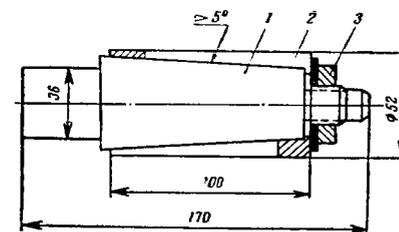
Притир для диаметра цилиндра 52 мм: 1—корпус притира; 2—размерная конусная втулка; 3—гайка.
